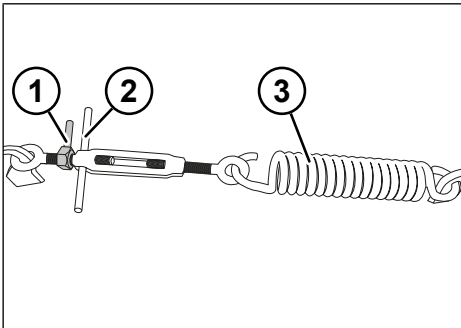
Zugfeder mit Spannschloss Ausführung 2
